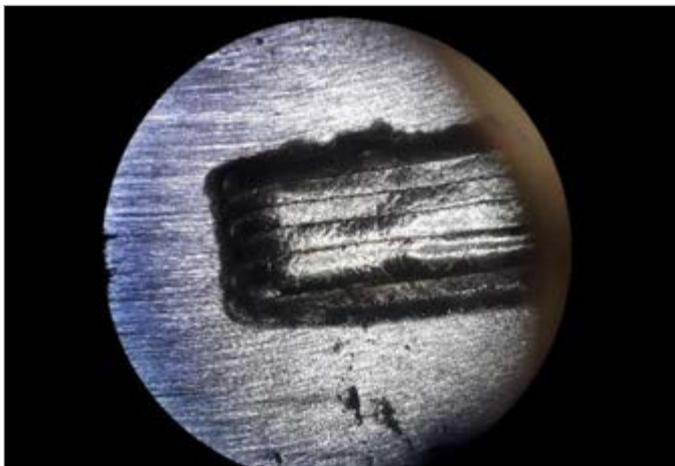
Auftragsschweißraupen mittels Laserstrahlschweißen an der Kompaktanlage
